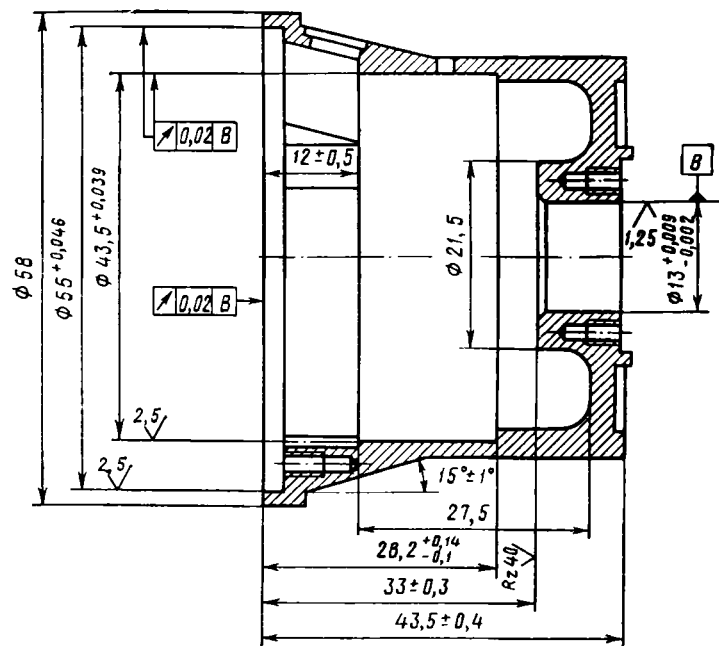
Корпус, совмещенный с подшипниковым щитом
